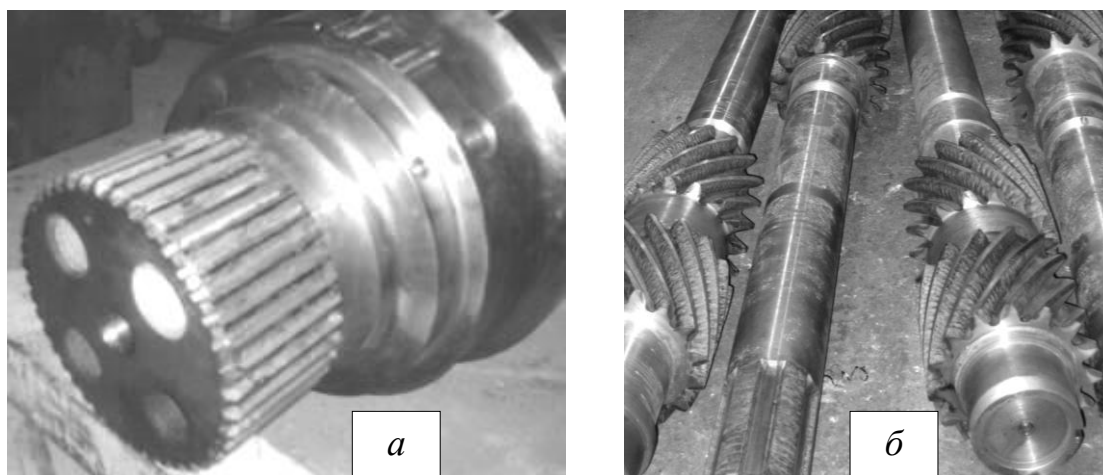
Крупногабаритные детали с плазменной закалкой:
